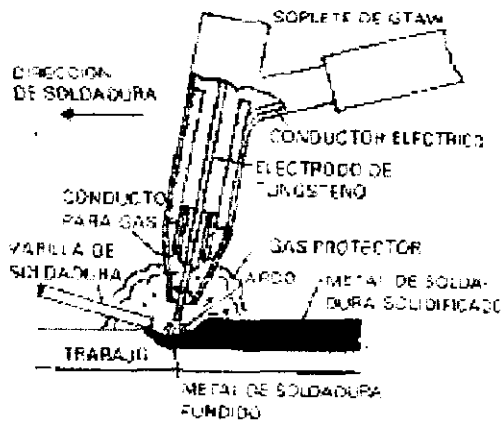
SOLDADURA CON GAS Y ARCO DE TUNGSTENO.
